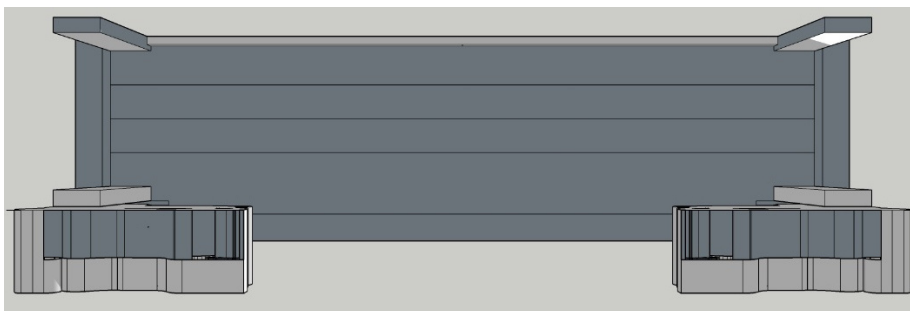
Vista do alçado inferior, ou fundo do armário. Fonte: própria
